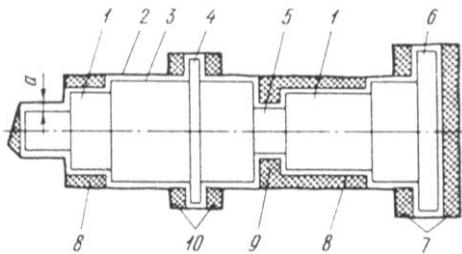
Припуски и напуски поковки ступенчатого вала:
